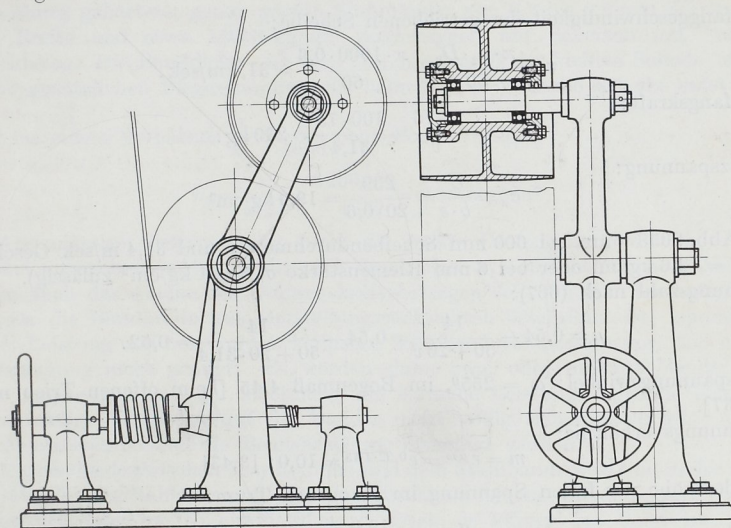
Senkrecht angeordneter Spannrollentrieb. Peniger Maschinenfabrik und Eisengießerei, Penig.
